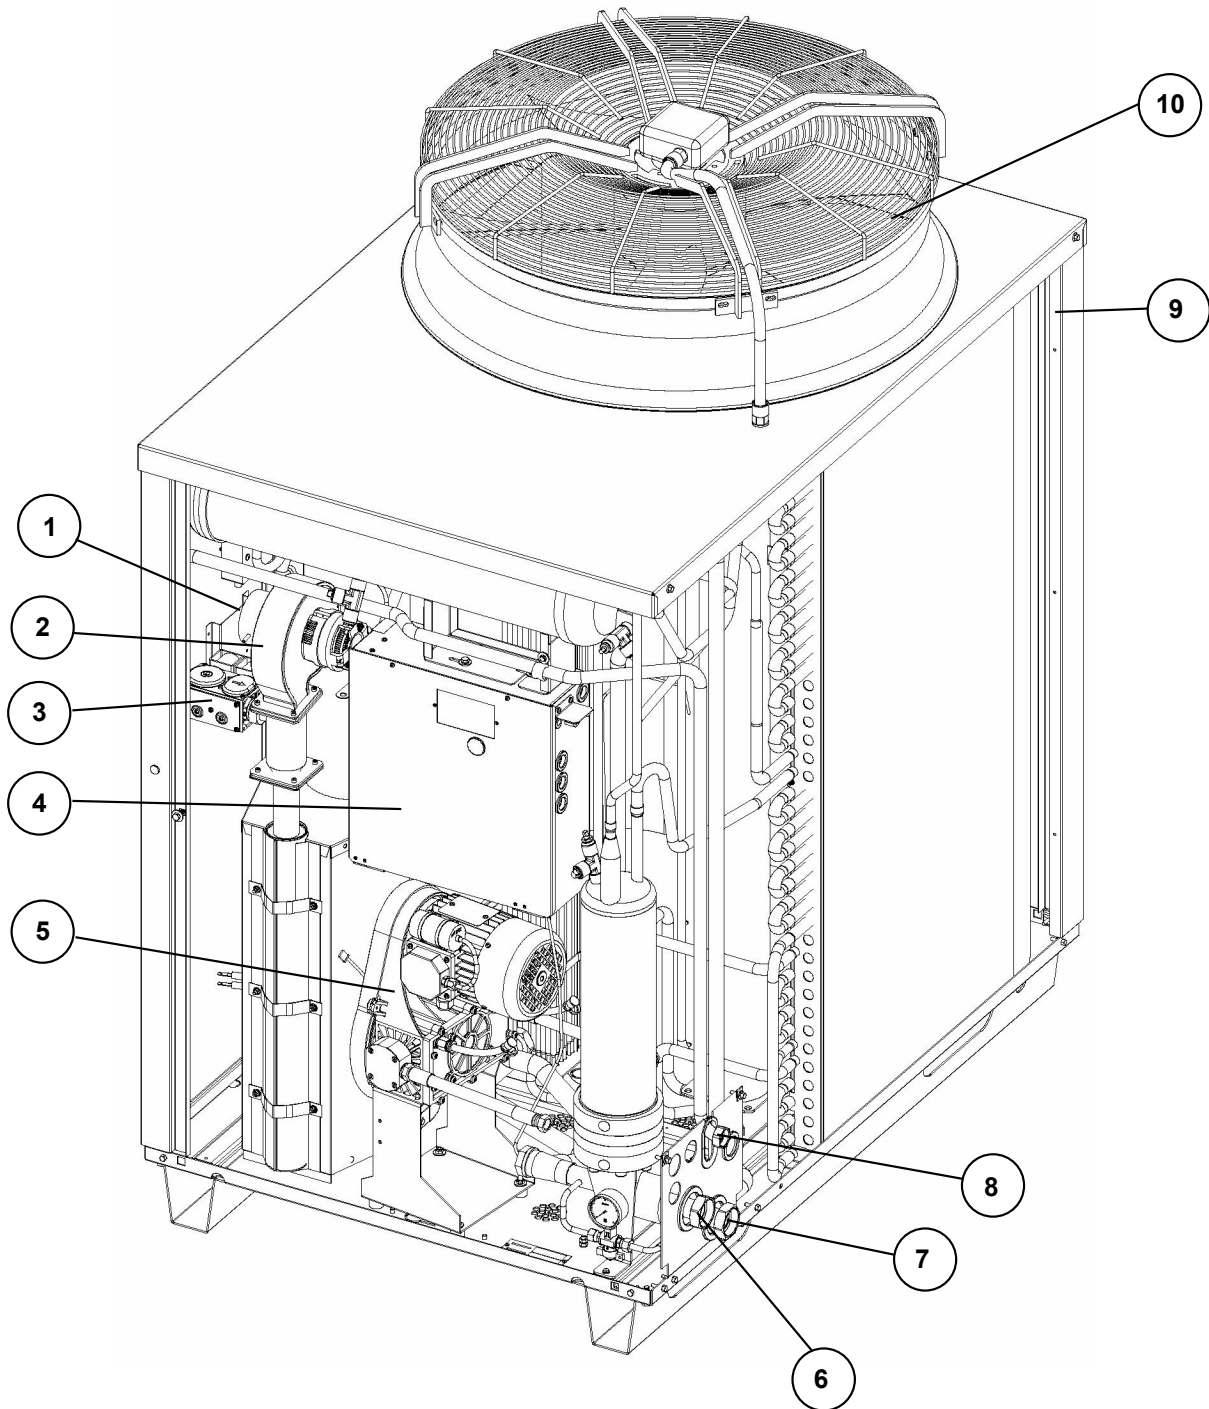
ACF-HR panel przyłączy - przyłącza hydrauliczne i gazu
